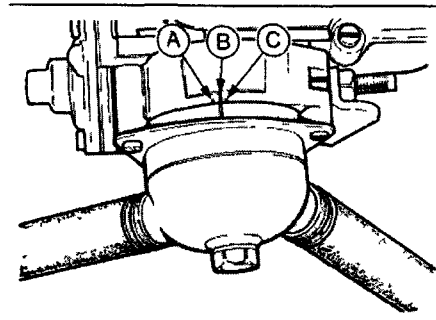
,б. Метки совмещения корпуса биметаллической пружины с корпусом карбюратора
